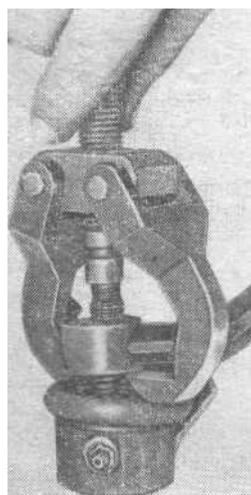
Выпрессовывание шарового пальца наконечника рулевой тяги из головки поворотного рычага (или рулевой сошки) при помощи съемника
